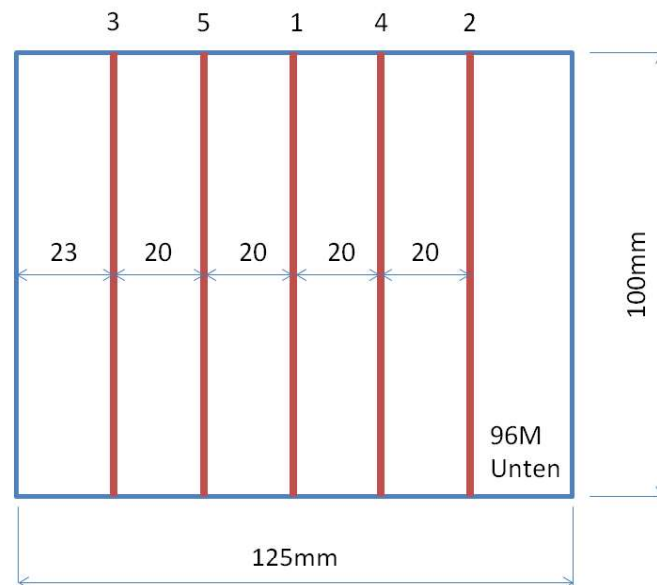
Skizze mit Probenabmessungen und Schweißvorlage für Blindschweißungen
